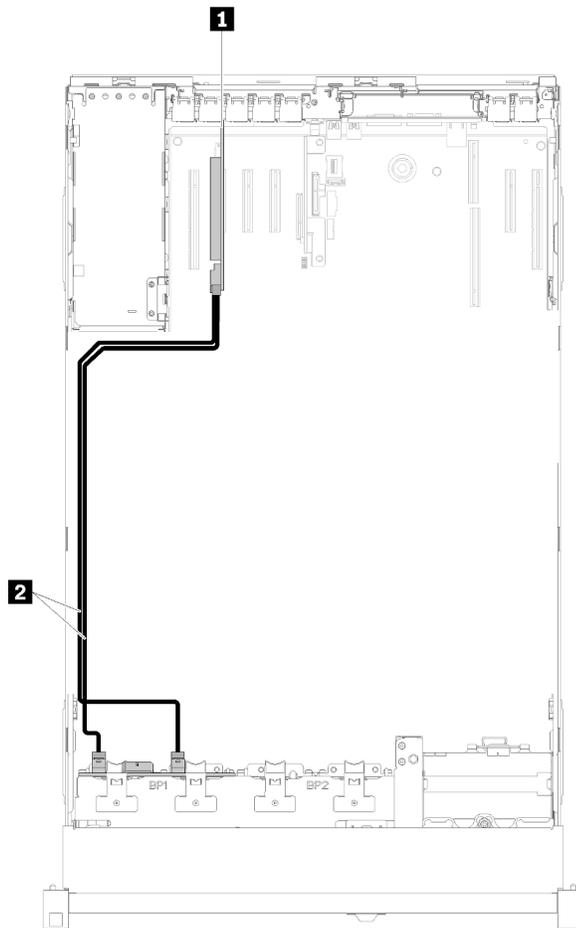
Instradamento dei cavi, Backplane a 8 vani
